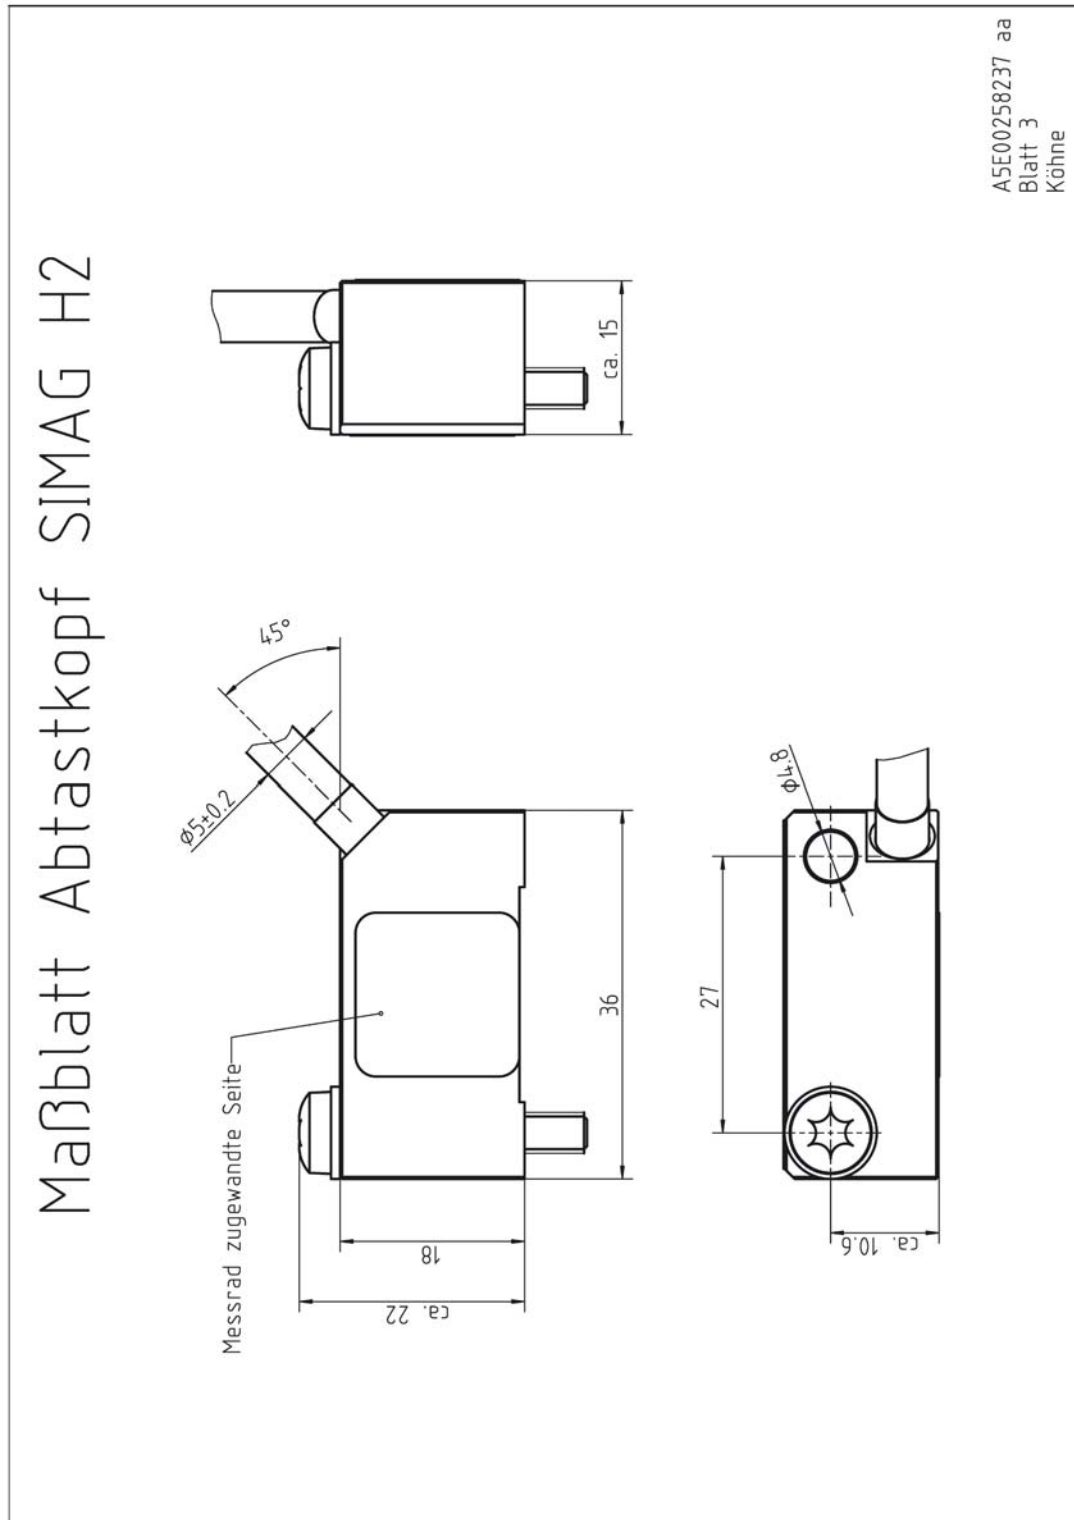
Габаритный чертеж считывающей головки SIMAG H2
